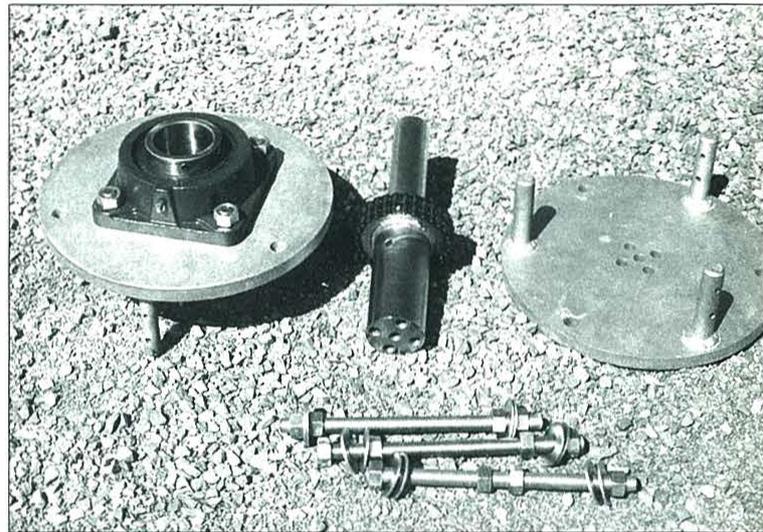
Componentes del conjunto del cojinete principal de giro del sistema Rotating Tower System (RTS) diseñado por Dick Weber, K5IU. (Fotos del autor).
